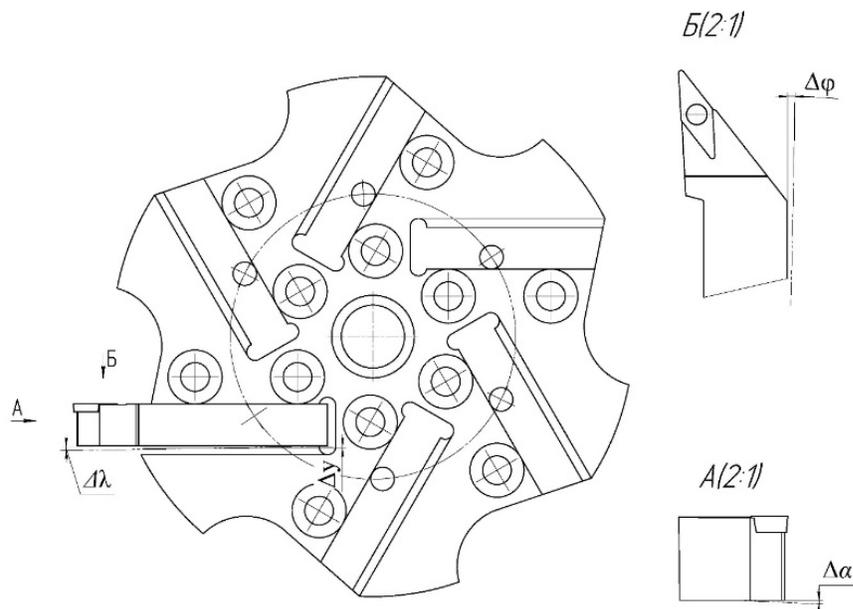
Эскиз револьверной головки мод. УГ9321.
